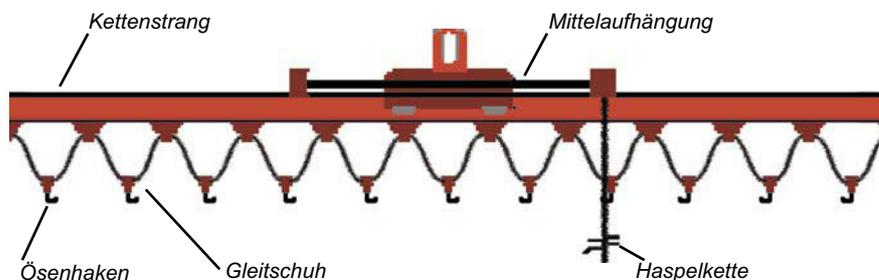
Ausschnitt Ausgleichstraverse (Beispielhafte Darstellung)
